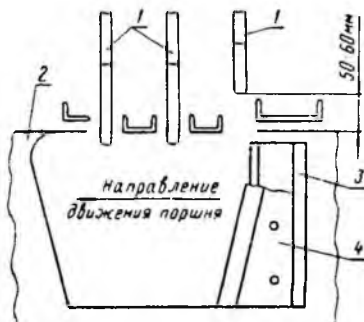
Положение переднего упаковщика у пресс-подборщика ПСБ-1,6 относительно прессовальной камеры в момент подхода поршня к загрузочной воронке:
